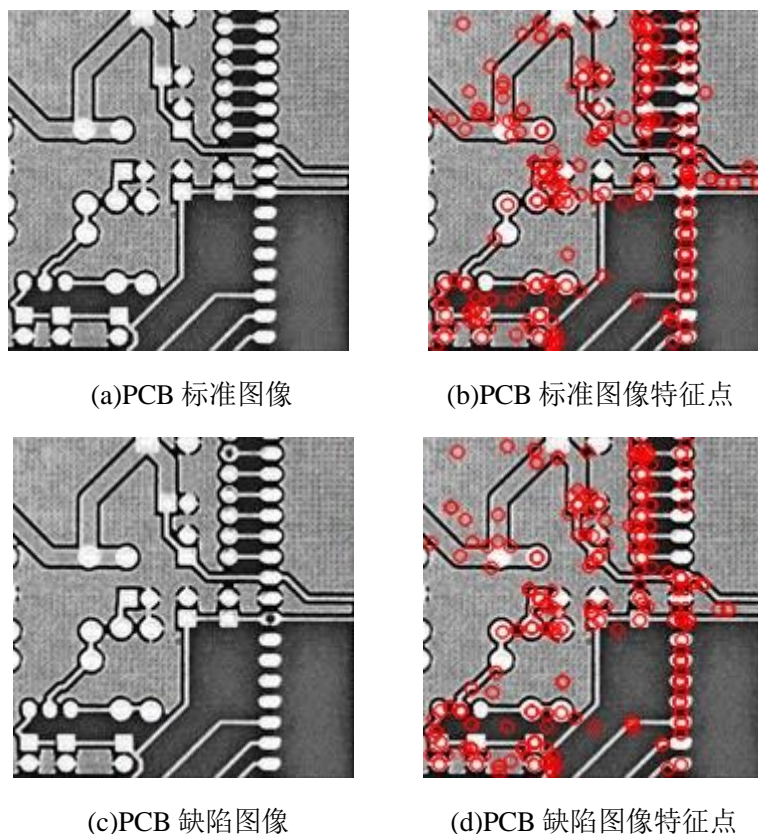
PCB 标准图像与缺陷图像特征提取对比
